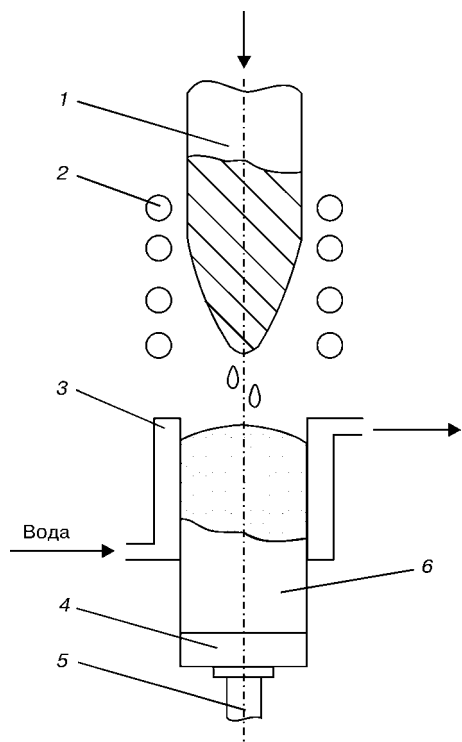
Схема индукционного переплава расходуемой заготовки с получением слитка в охлаждаемом кристаллизаторе [1]: 1 — расходуемая заготовка; 2 — индуктор; 3 — кристаллизатор; 4 — поддон; 5 — шток механизма вытягивания слитка; 6 — слиток
